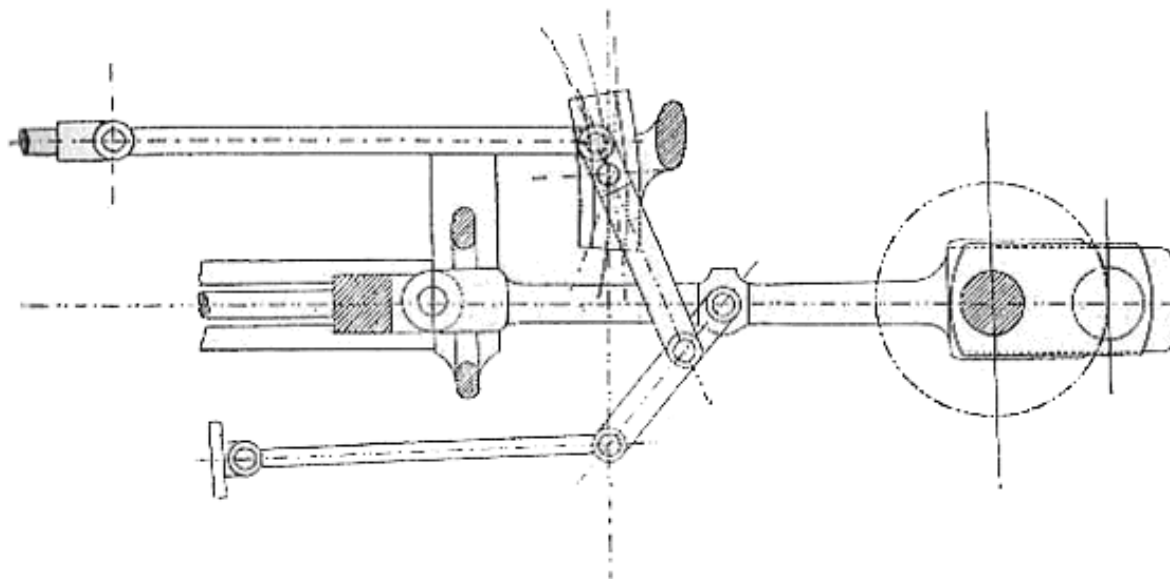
Distribución Joy: el taco está representado en su posición media: líneas punteadas indican las posiciones extremas de marcha adelante y atrás. El taco desliza en el sector; el vástago de la corredera se muestra en la parte superior izquierda de la figura.
